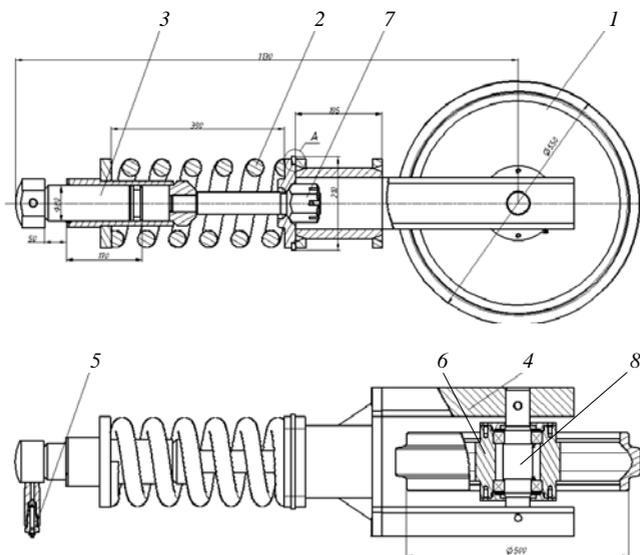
Схема к регулировке натяжения гусеницы и подшипников натяжных колес: 1 – натяжное колесо; 2 – пружина; 3 – цилиндр; 4 – ползун; 5 – масленка; 6 – ступица; 7 – шток; 8 – ось
